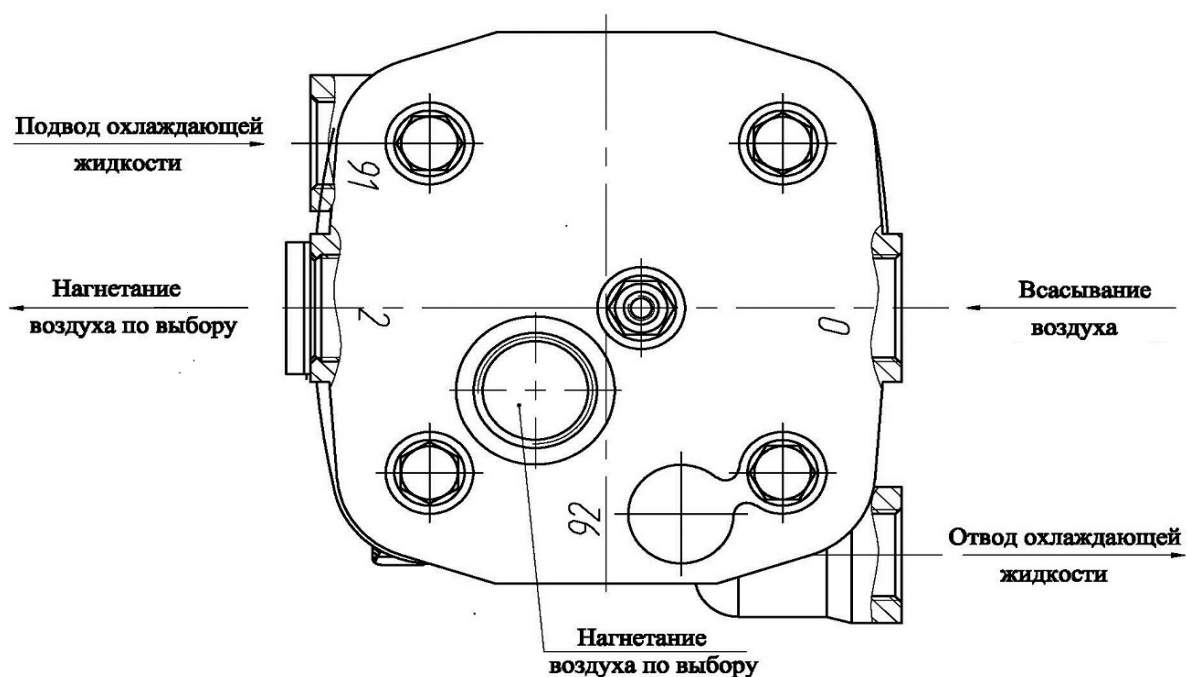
а. Расположение всасывающих и нагнетательных патрубков, а также отверстий подвода и отвода охлаждающей жидкости компрессора АМ.3509015-03.
